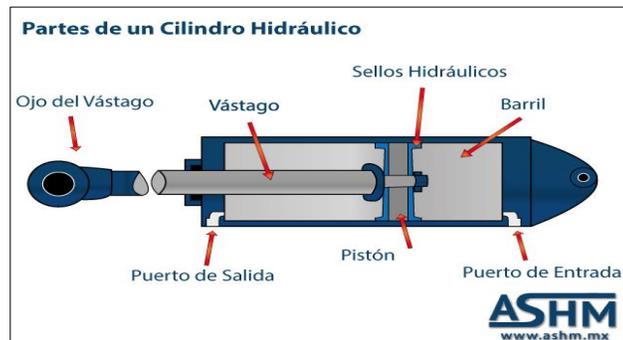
Vista en Corte de un Cilindro Hidráulico.
